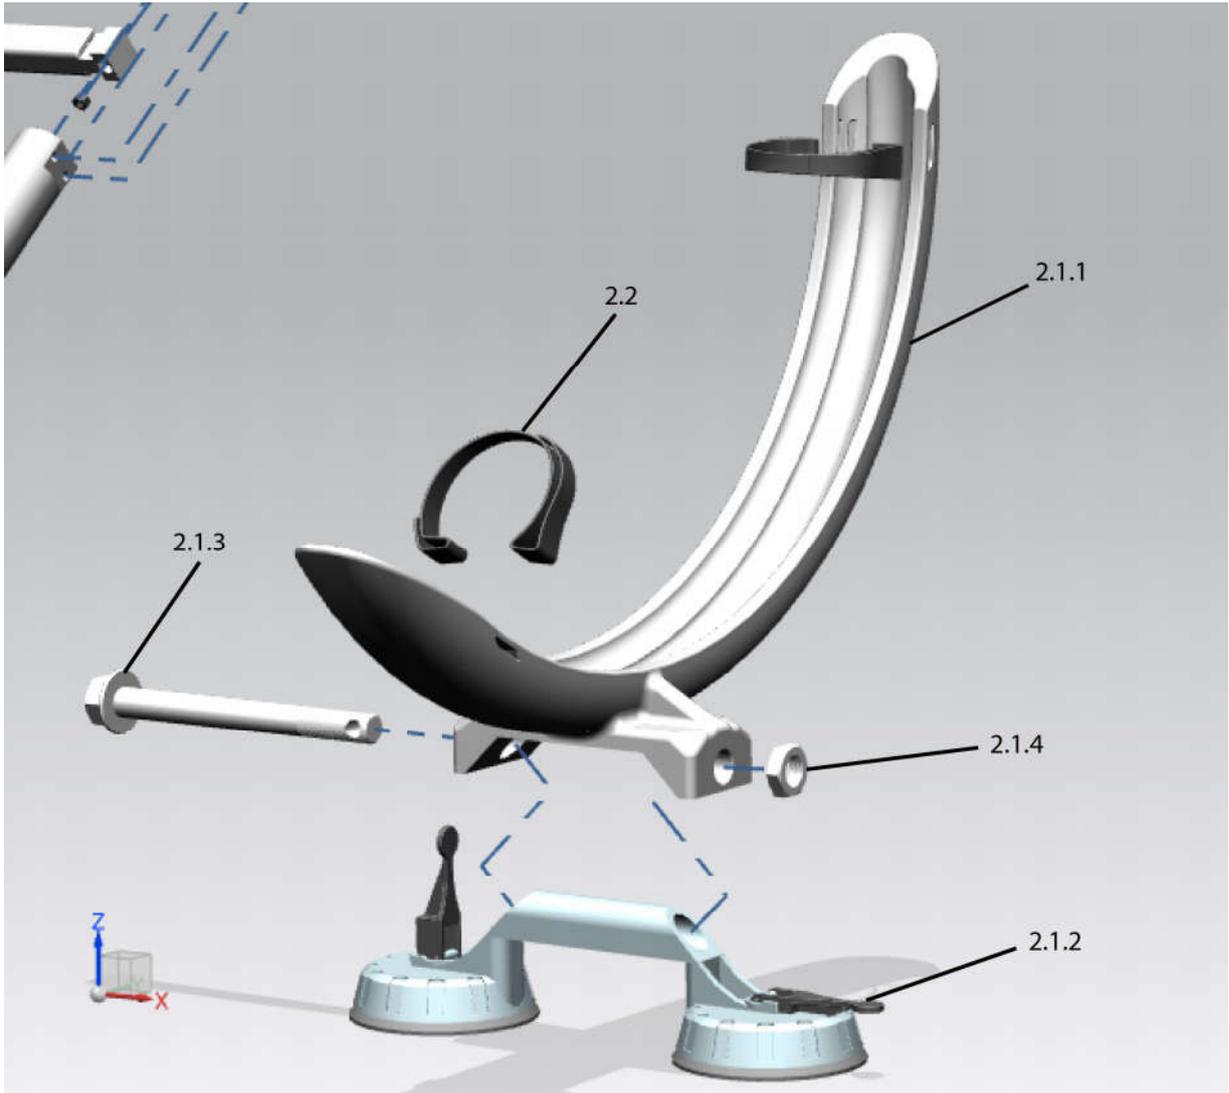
Vista explosionada de detalle. Subconjunto trasero.
